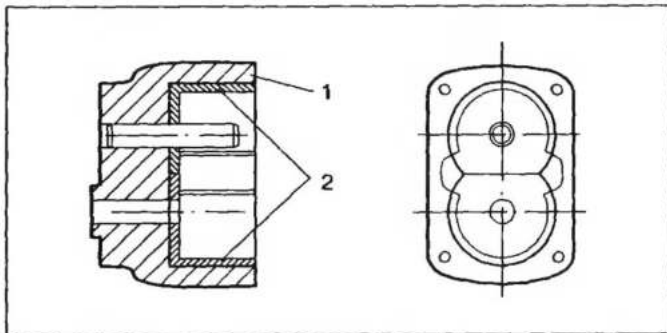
Ремонт изношенных поверхностей под шестерни в корпусе масляного насоса:
